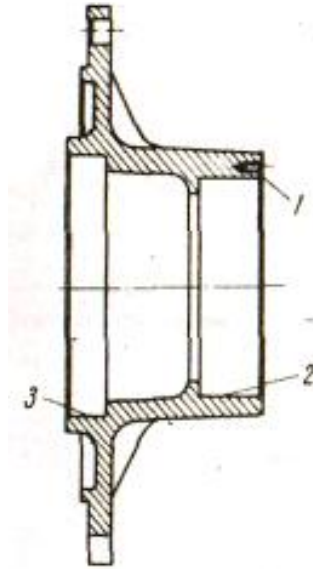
Картер планетарного редуктора 151.39.102-2. Схема дефектів
